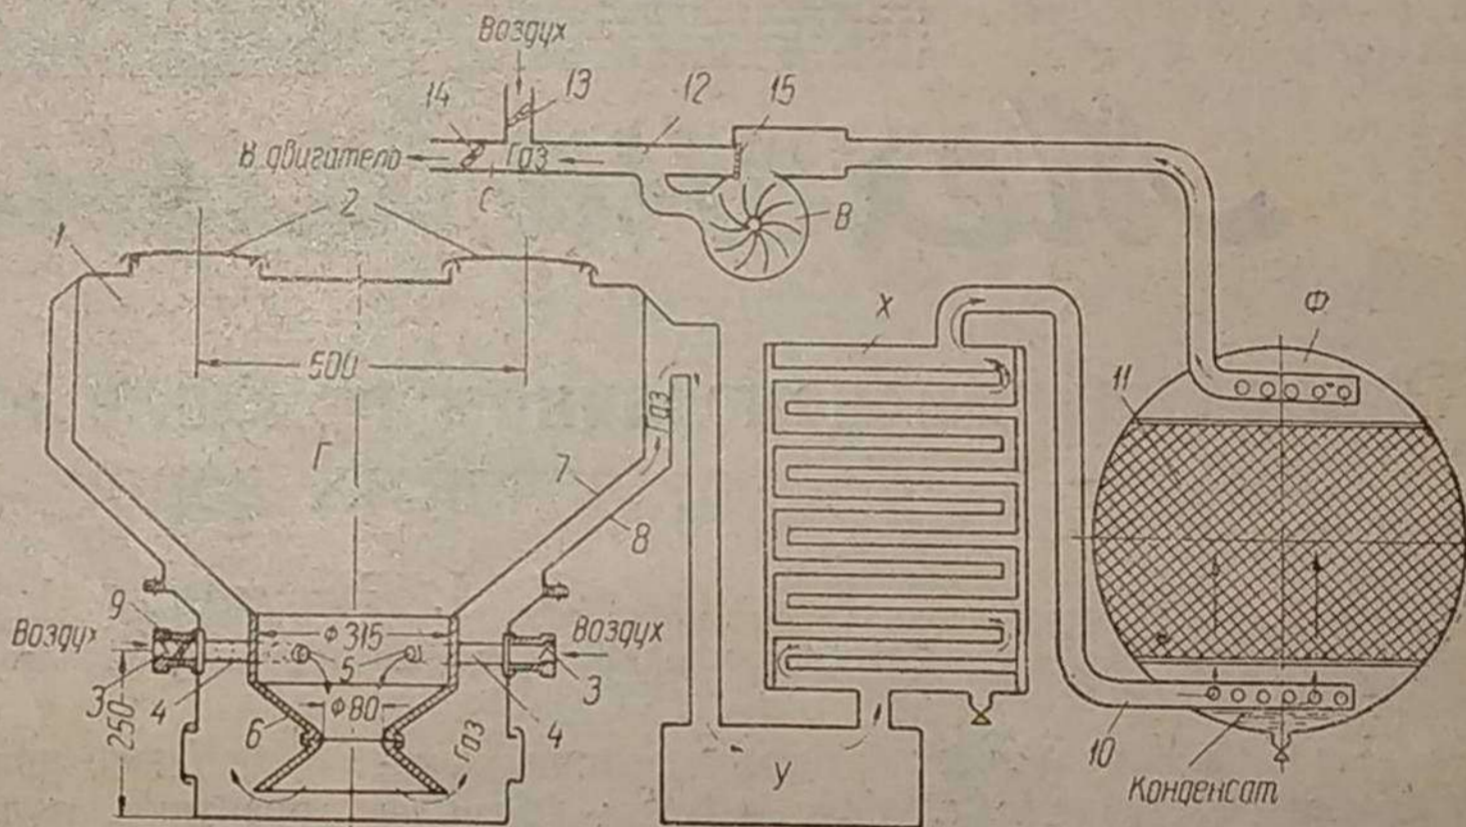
Схема газогенераторной установки Пельцера для автомобиля М-1
